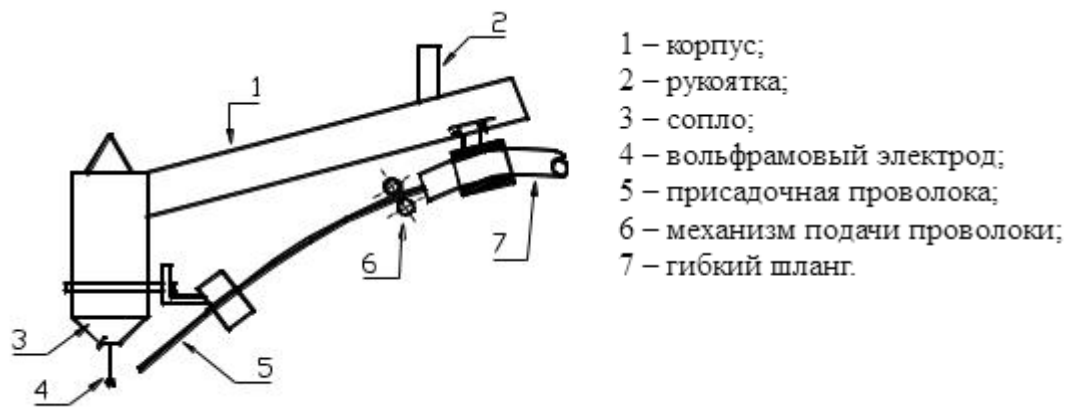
Схема механизированной сварки неплавящимся электродом
